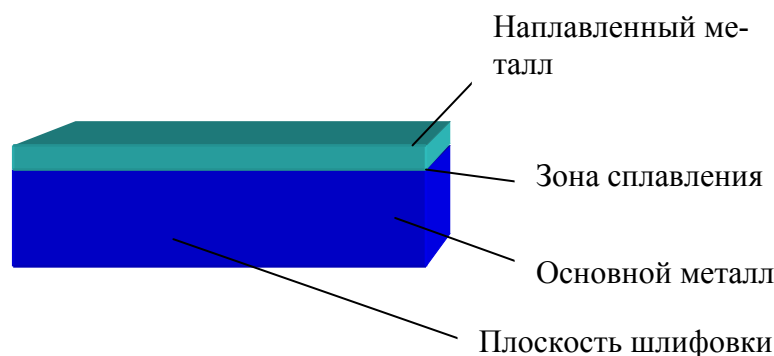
Структура наплавленного образца и плоскость шлифовки
